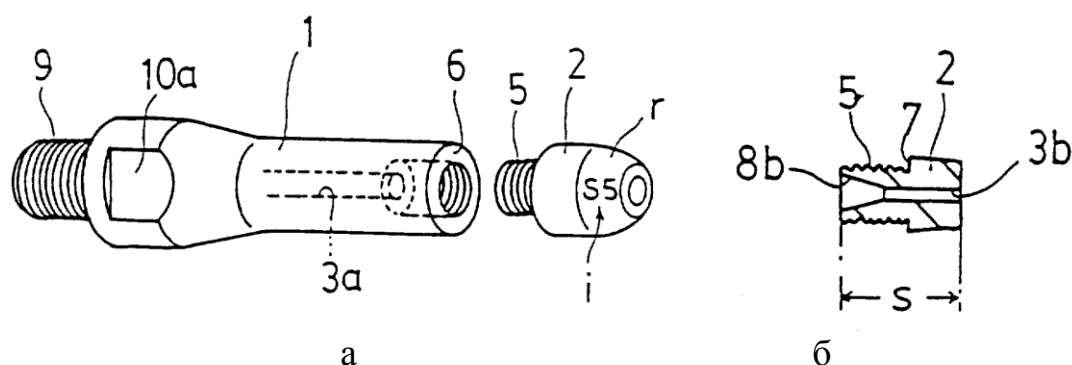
Контактный наконечник (а) для сварочной горелки и головка к нему (б) по патенту России № 2118242
